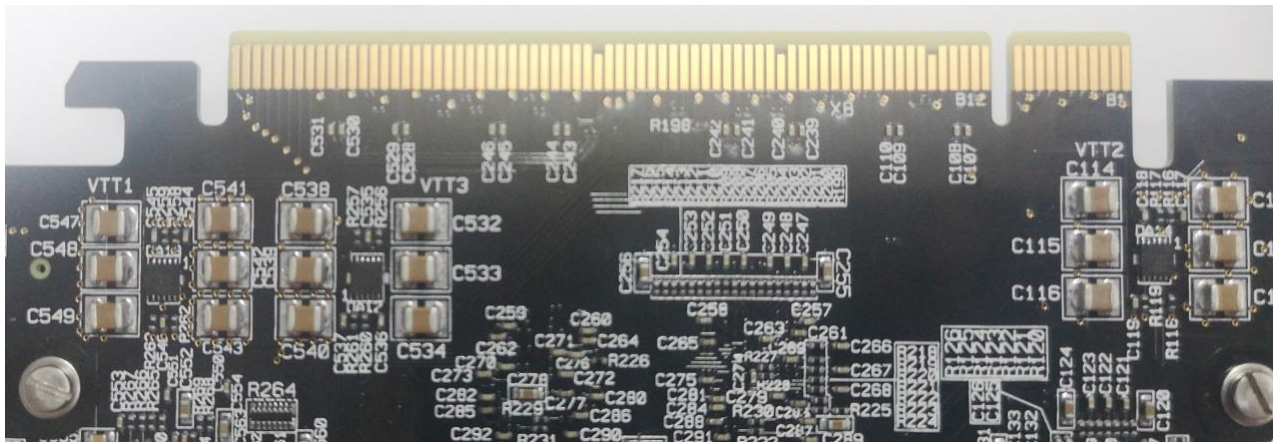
Соединитель X8 Модуля. Вид снизу
